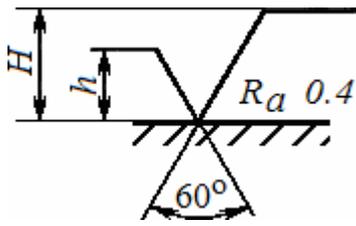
Структура знака изображения шероховатости поверхности детали на чертеже
